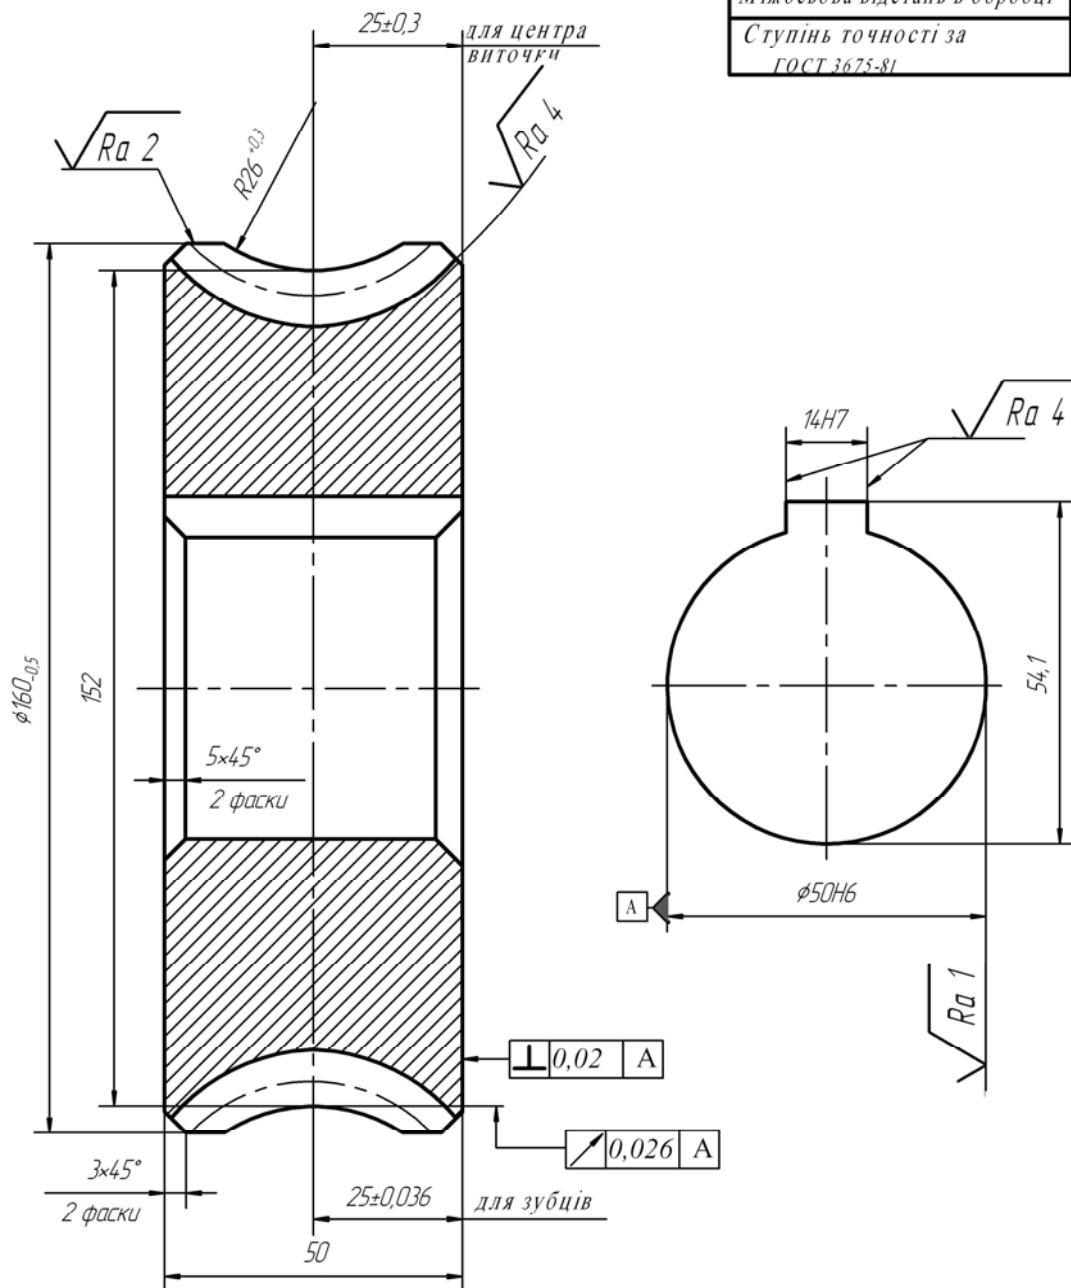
Приклад робочого кресленика черв'ячного колеса
